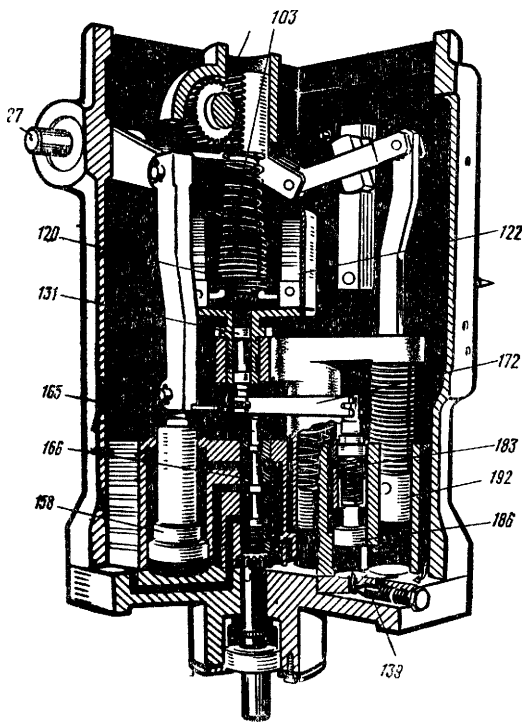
27—выходной вал; 103—задающая пружина; 120—муфта с подшипником; 122 — грузы регулятора; 131 — шток; 139 — игла изодрома; 158—поршень сервомотора; 165 — распределительный золотник; 166 — втулка распределительного золотника; 172— плавающий рычаг; 183 — пружина изодрома; 186 — принимающий поршень изодрома; 192—задающий поршень изодрома
